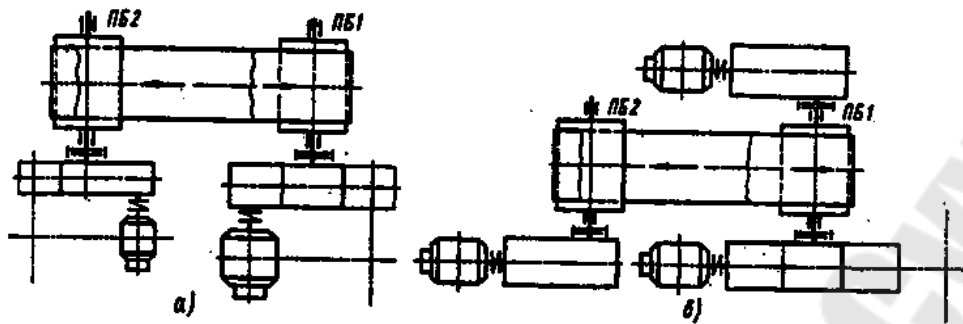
Схемы приводных механизмов двухбарабанного привода с электродвигателями: а - двумя; б - тремя; ПБ - приводной барабан.
